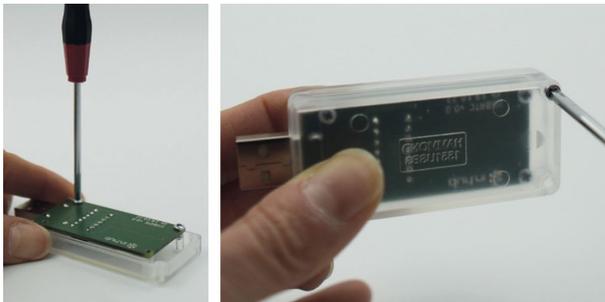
Platine und Gehäuse wieder zusammenschrauben
